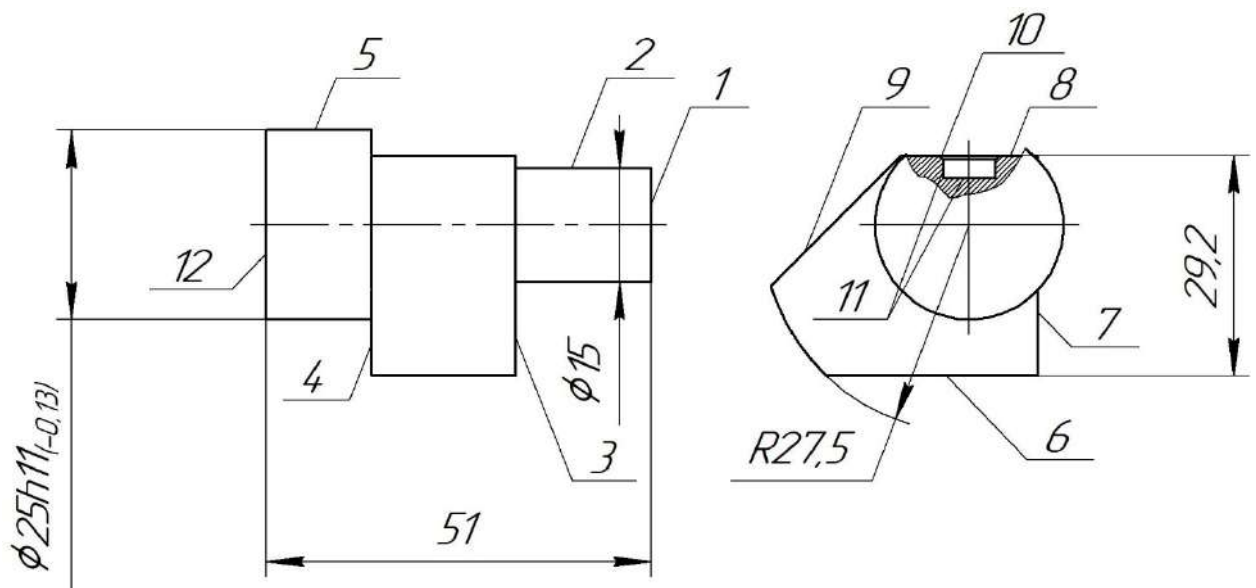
Проміжна заготовка корпусу Р30.00.921-01 з позначенням нумерації поверхонь, оброблених на першому етапі (підготовча обробка корпусу перед складальною операцією)
